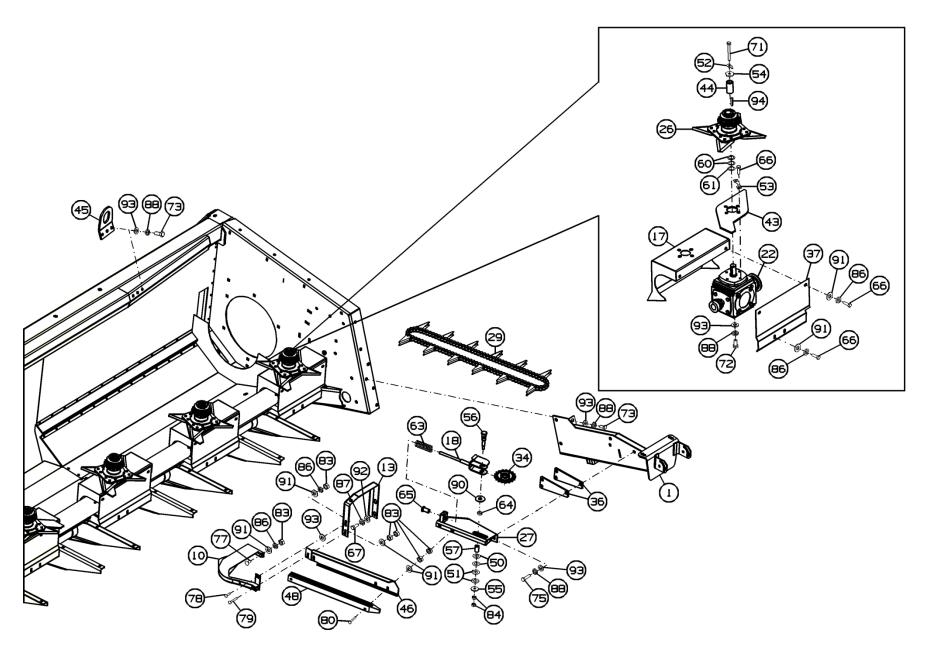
Корпус жатки ПСП-620.01.01.000
